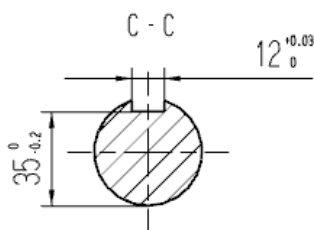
标注剖视图 C-C 的尺寸 (二)
